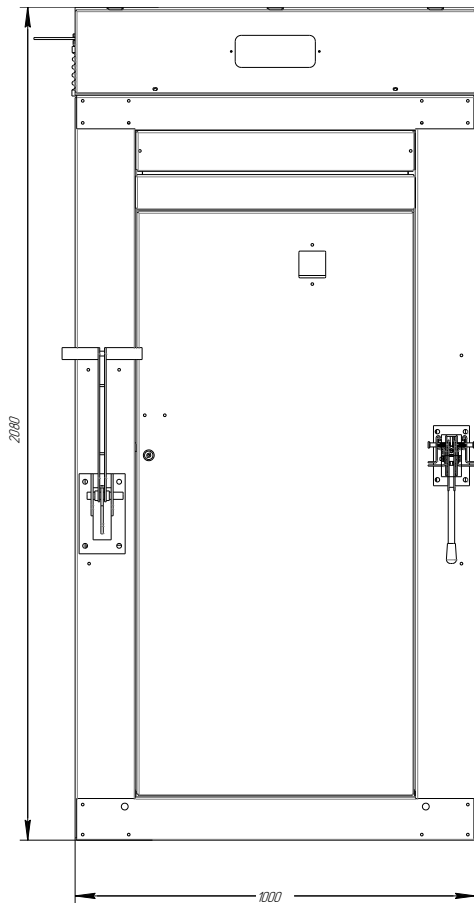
Габаритные размеры камеры КСО - 303 - 01
